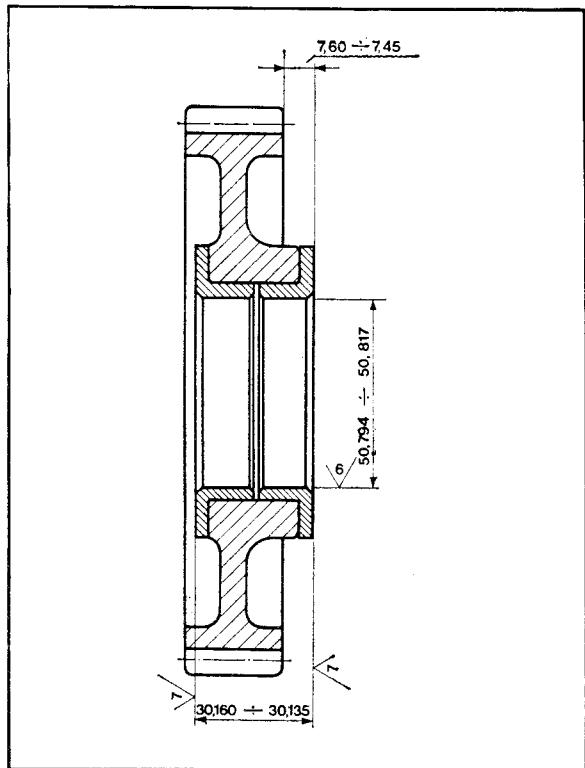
A.34 – Zupčanik pumpe za ubrizgavanje
